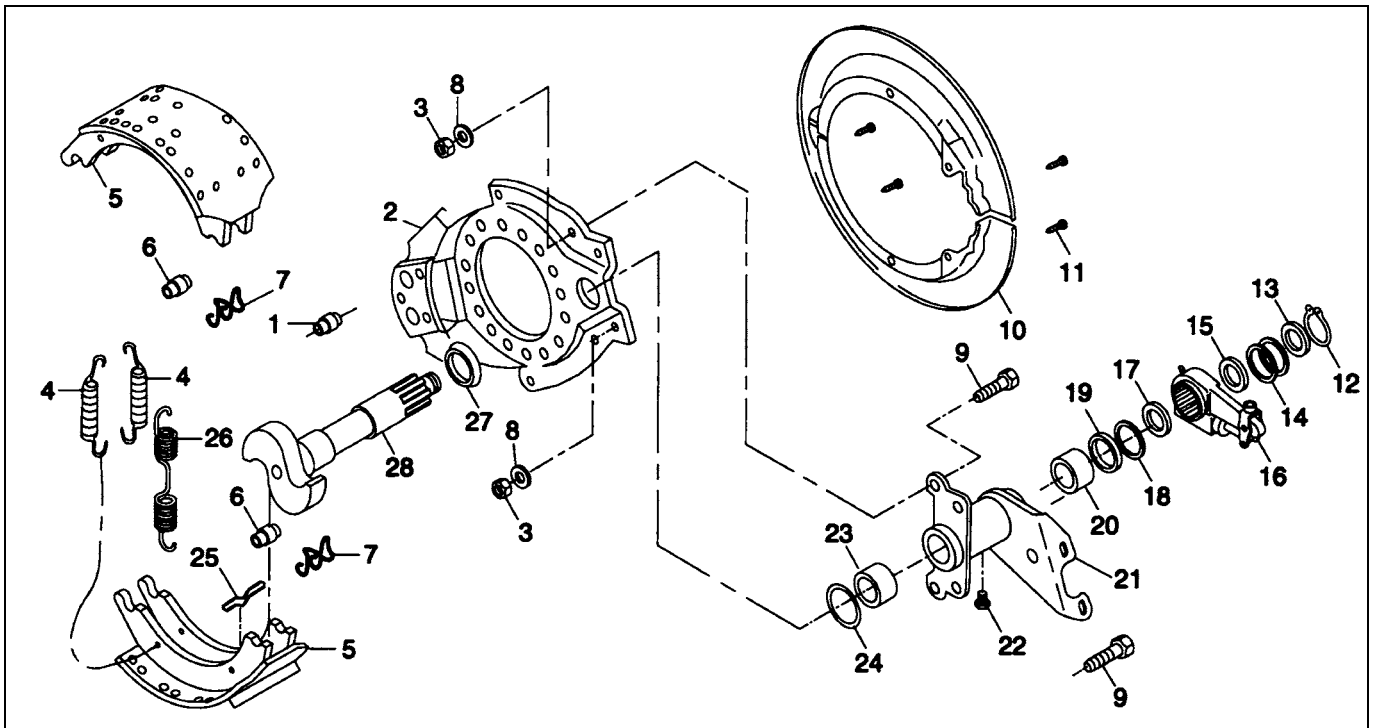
Тормоз Q Plus серии MX500 со штампованным опорным диском. 1 - анкерный палец, 2 - опорный диск, 3 - гайка (4 шт.), 4 - фиксирующая пружина, 5 - тормозная колодка в сборе, 6 - ролик кулачка, 7 - клипса ролика, 8 - закаленная шайба (4 шт.), 9 - болт (4 шт.), 10 - пыльник, 11 - болт пыльника, 12 - стопорное кольцо кулачкового вала, 13 - шайба/прокладка, 14 - тонкая прокладка, 15 - оранжевый сальник, 16 - автоматический компенсатор износа, 17 - сальник, 18 - толстая прокладка, 19 - сальник, 20 - втулка кулачкового вала (1-1/2 дюйма), 21 - кронштейн кулачкового вала и тормозной камеры, 22 - пробка, 23 - втулка кулачкового вала (1-5/8 дюйма), 24 - оранжевый сальник, 25 - палец возвратной пружины, 26 - возвратная пружина, 27 - упорная шайба с фаской, 28 - кулачковый вал.
